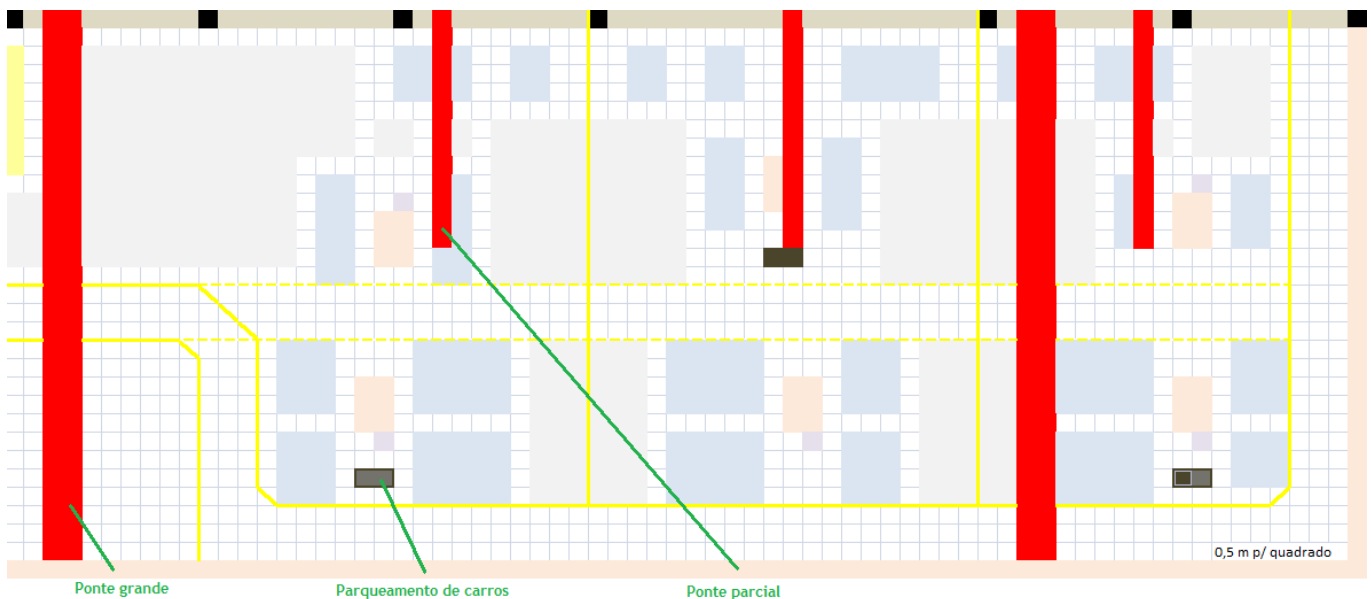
Layout final das pontes e carros nas Bancadas da IMA.
